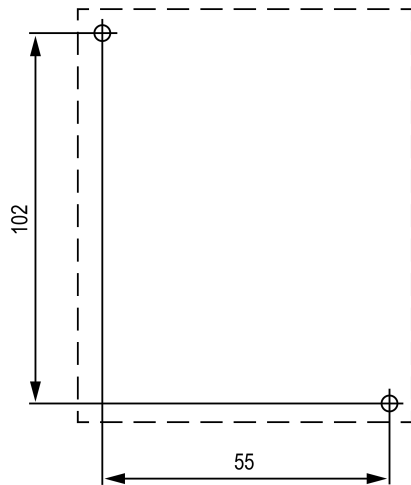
Габаритный чертеж ПР110-х.8х.4х
